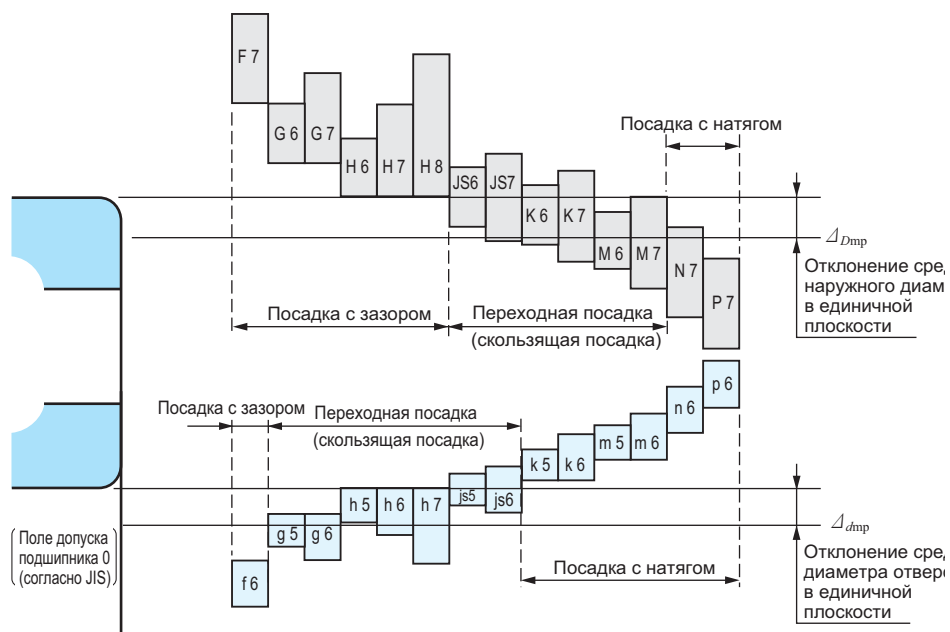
Соотношения между допусками на диаметры валов / отверстия корпусов и посадками (подшипники класса точности 0)
